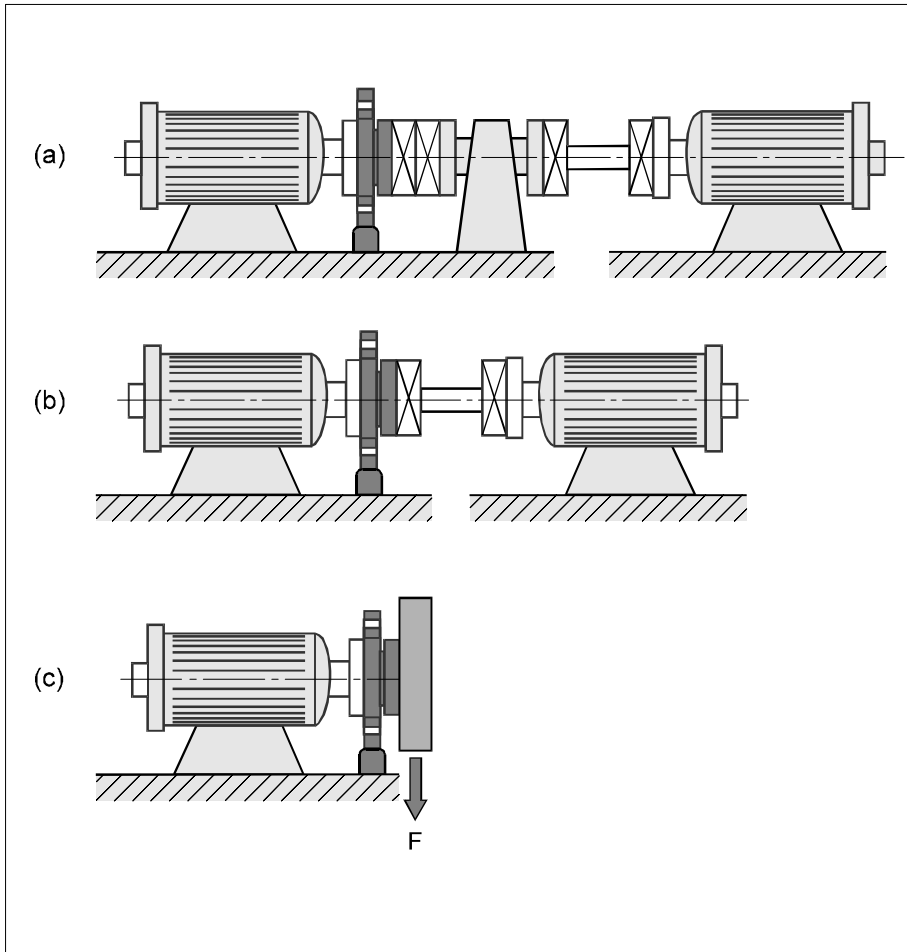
Einbauvarianten für Drehmoment-Messflansche
